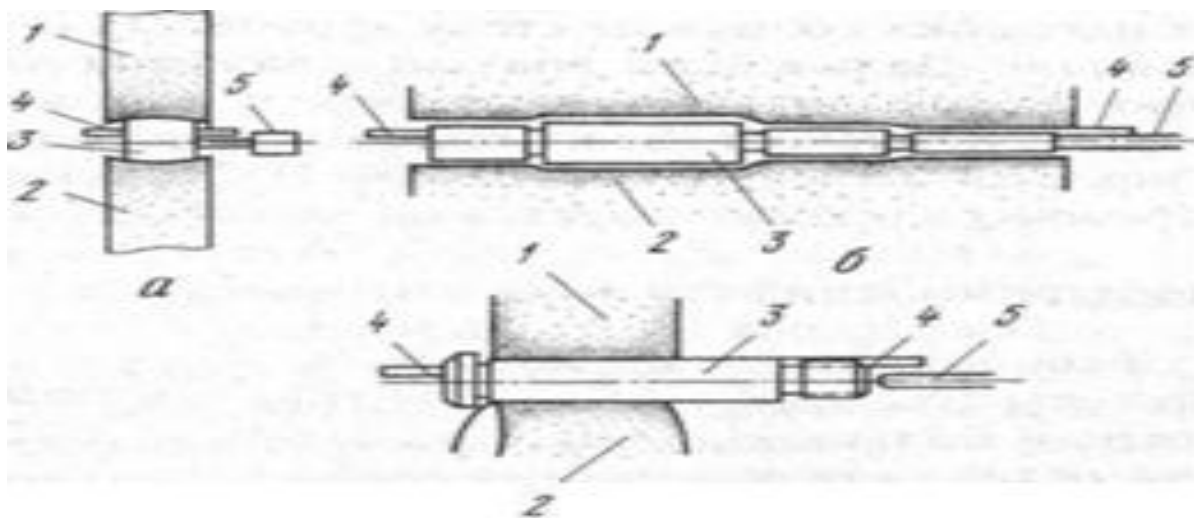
Методы бесцентрового шлифования: а, б – врезное, в – до упора: 1 – шлифовальный круг, 2 – ведущий круг, 3 – заготовка, 4 – опорный нож, 5 – упор.
